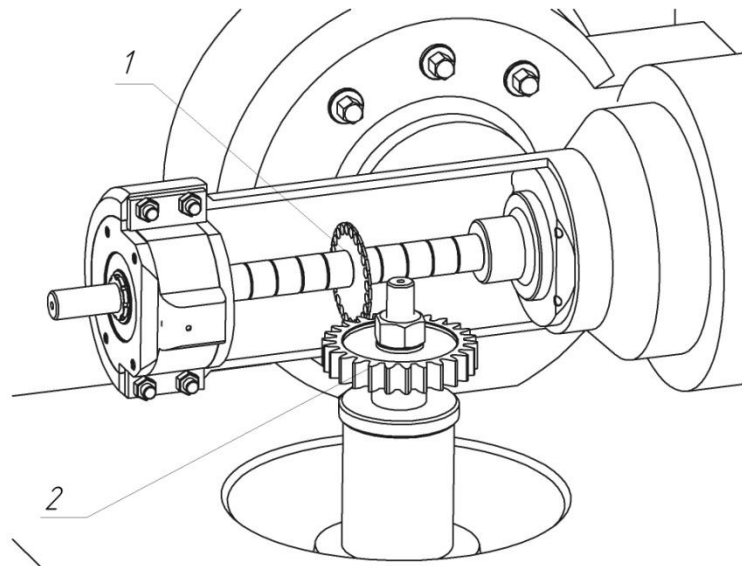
Схематичне зображення встановленого дискового інструмента та циліндричного зубчастого колеса на зубофрезерний верстат мод.5А312
